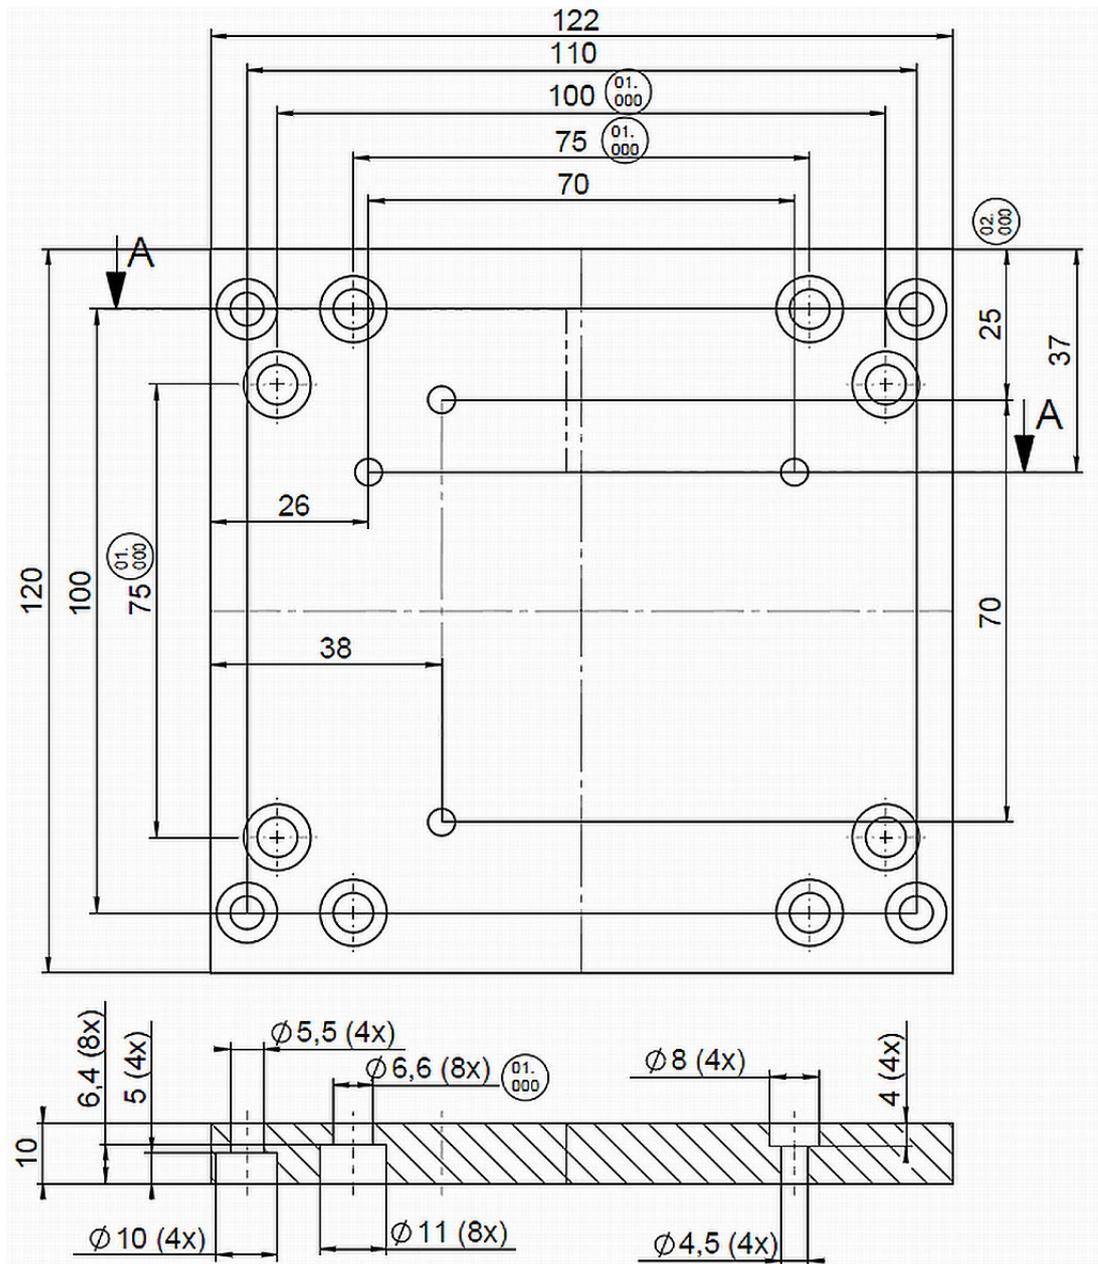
Abmessungen Montageadapter M-413.AP2
